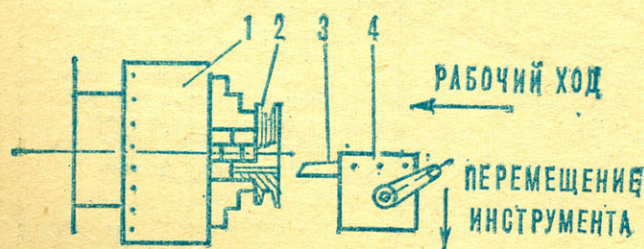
Токарный станок в роли долбежного: 1 — патрон токарного станка, 2 — обрабатываемая деталь (например, шкив), 3 — резец, 4 — резцедержатель.
